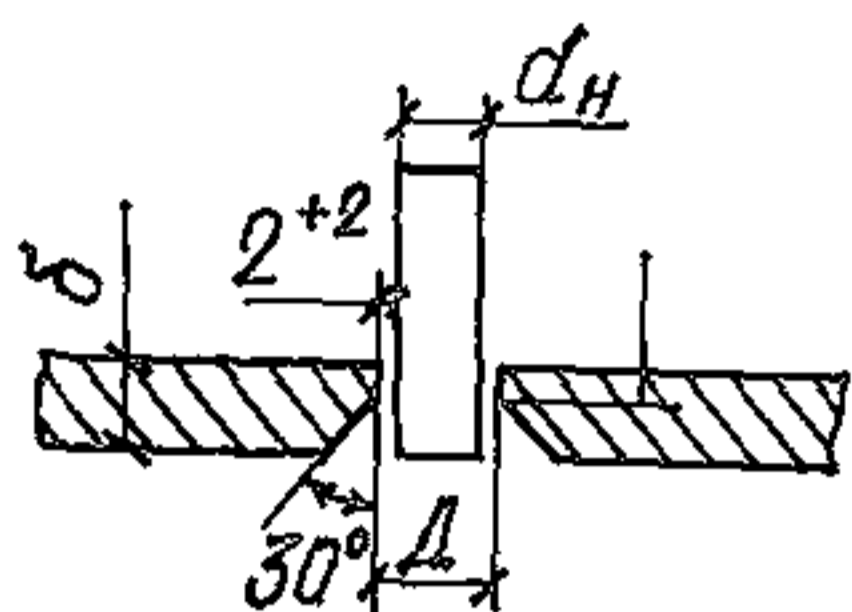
Конструкция таврового соединения, выполняемого ручной дуговой сваркой с предварительным устройством в плоском элементе отверстия с раззенковкой
